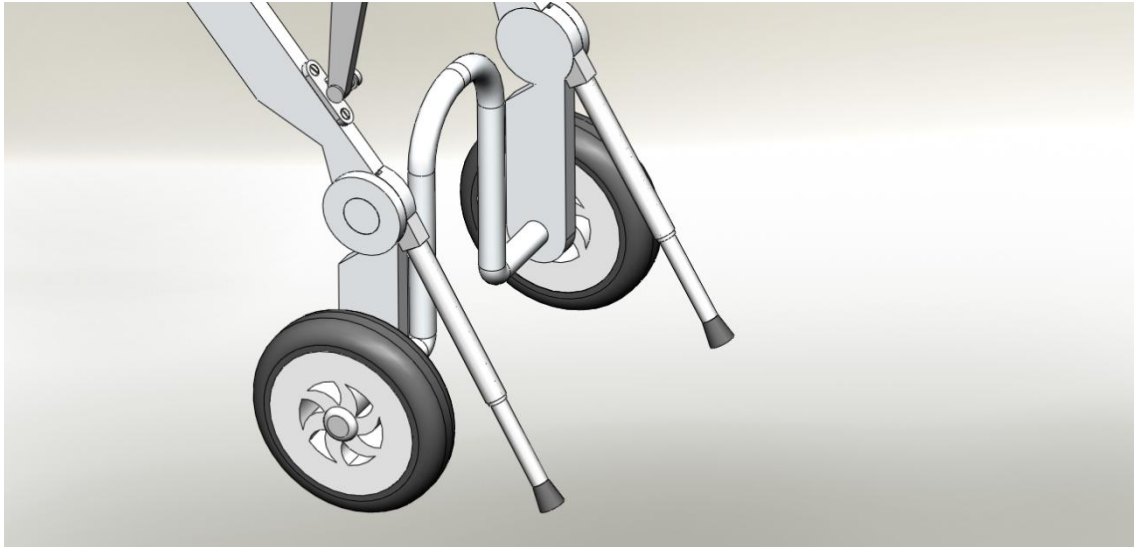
Colocación de la palanca de apoyo en la silla (fuente propia)
